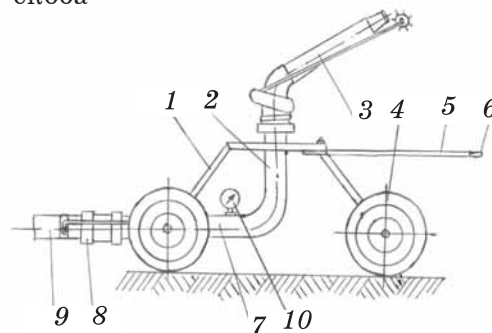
Передвижная тележка: 1 — рама; 2 — стойки; 3 — дождевальная аппаратура; 4 — колесо; 5 — водило; 6 — ручка; 7 — подводная труба тележки; 8 — муфта; 9 — трубопровод; 10 — манометр
